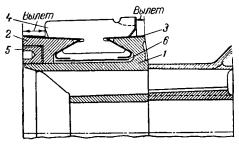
Продольный разрез коллектора. 1 — коробка или втулка; 2 — нажимная шайба; 3—изоляционный конус; 4 — пластина коллектора; 5 — гайка: 6 - изоляционный цилиндр.
